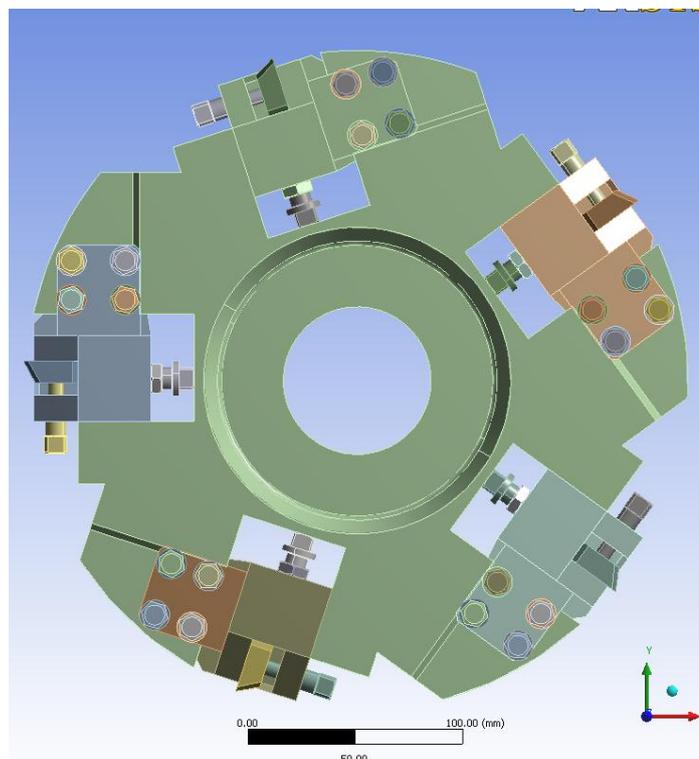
Сборочная модель фрезы (вид снизу)
